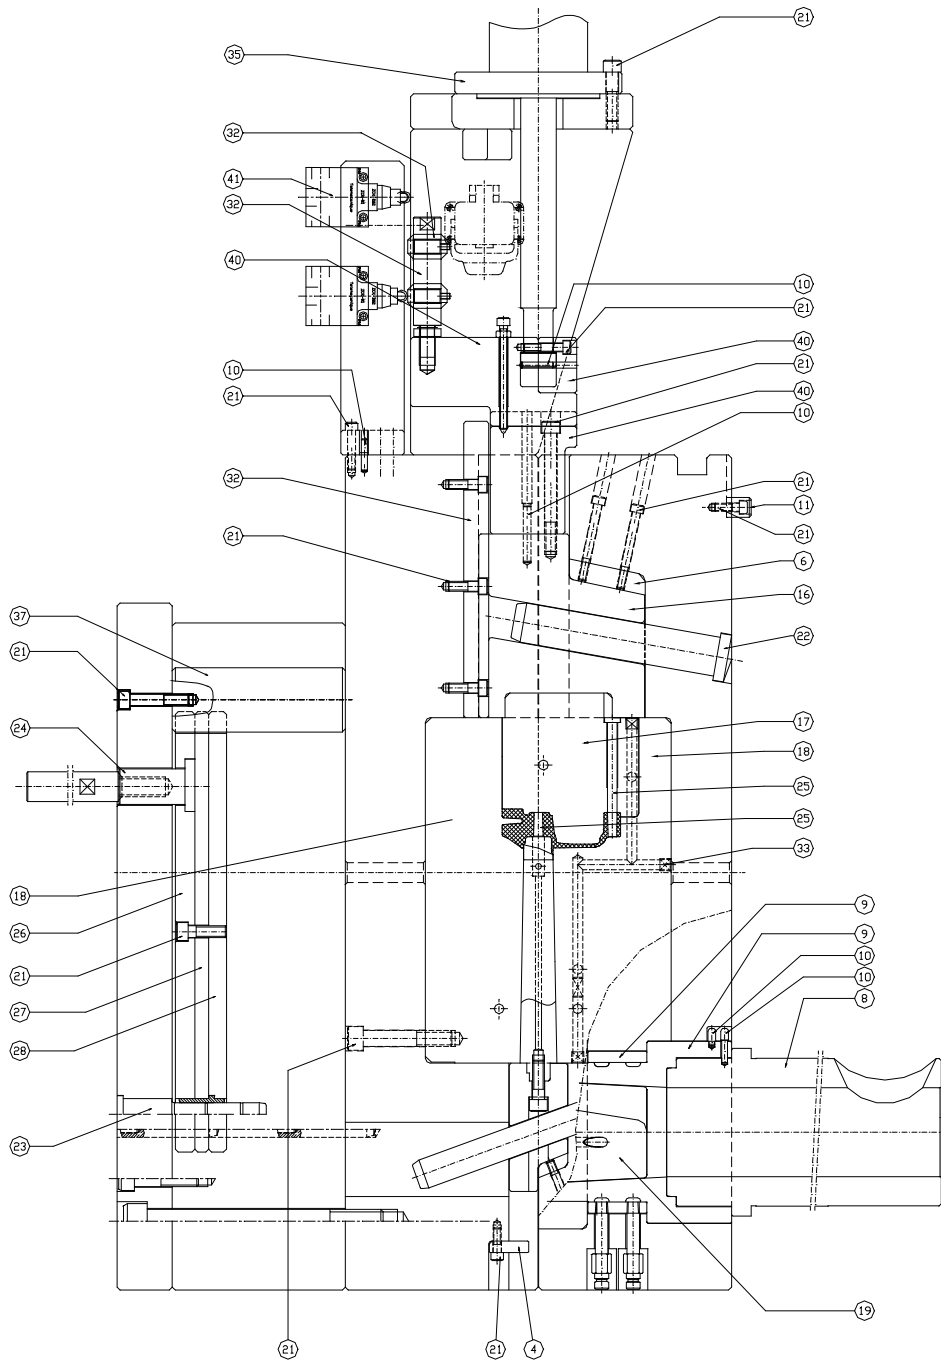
Desenho de conjunto do molde (vista esquerda) (4)
